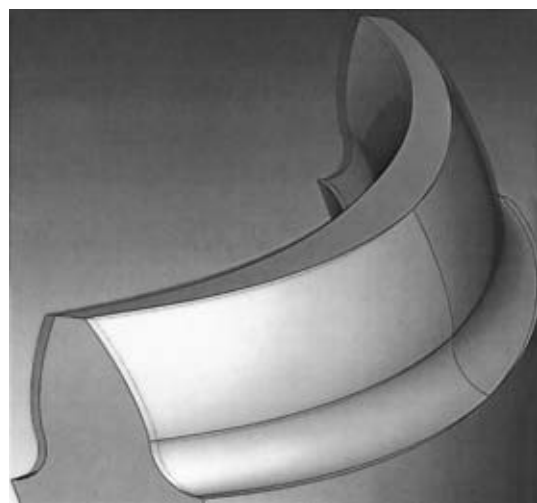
Бочкообразный зуб арочного цилиндрического колеса
